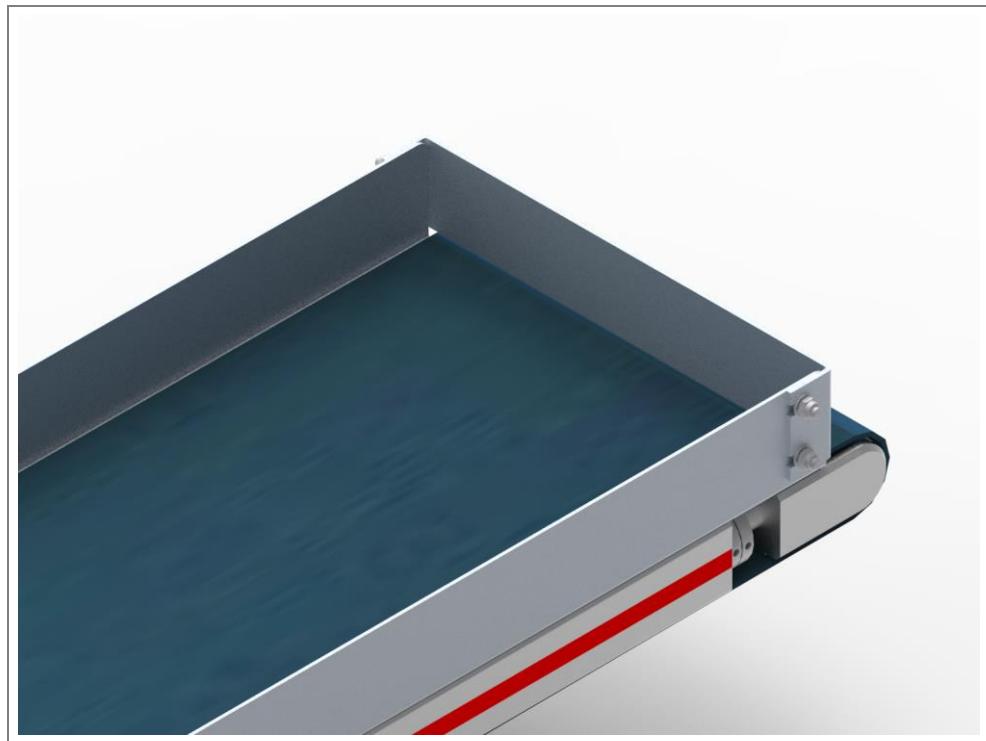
Dopravný pás so zadnou stenou a vratnou vaňou (príklad)
